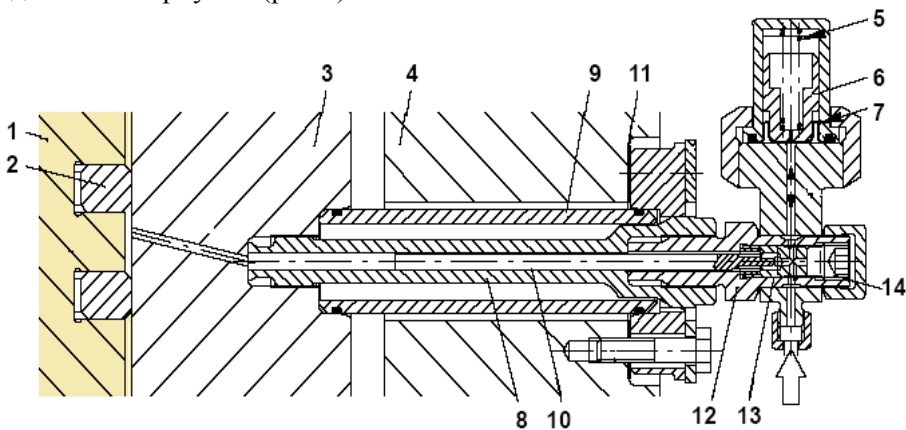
Составляющие 2-х рядной лубрикаторной системы двигателей RTA: 1-поршень двигателя; 2-поршневое кольцо; 3-цилиндрическая втулка; 4-рубашка; 5-пружина; 6-поршень аккумулятора; 7- мембрана; 8-корпус шту-
